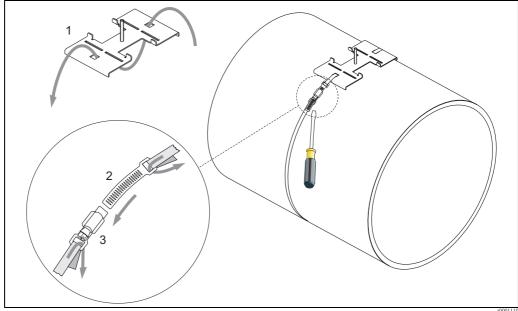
Premontaggio delle fascette di fissaggio per diametri del tubo DN >200
